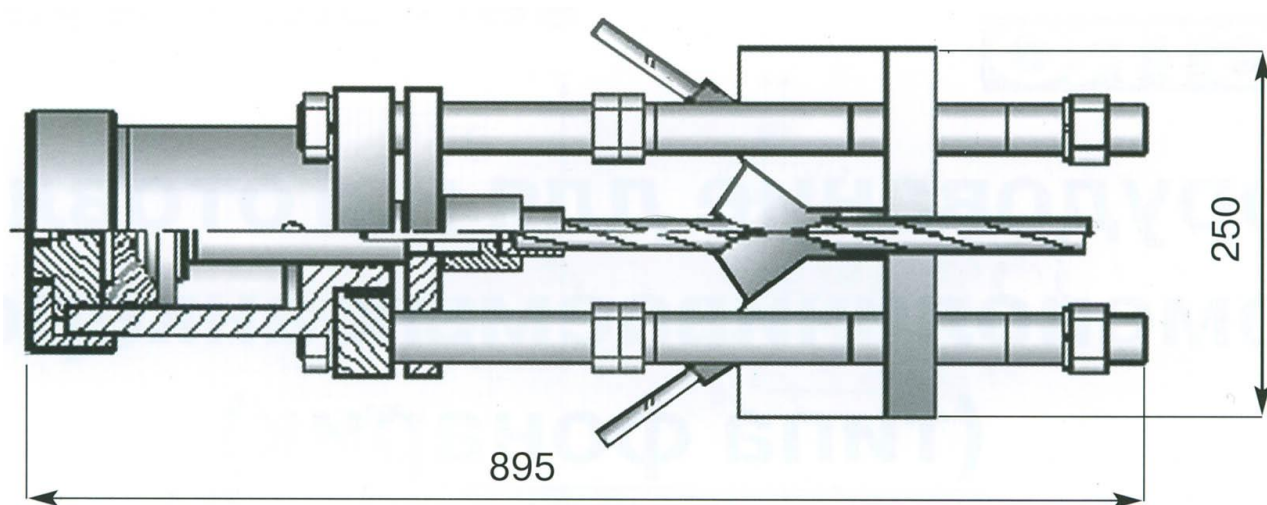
Стенд ГПФ-3 для осуществления расплетения проволок на конце каната 15К7 с формированием «фонарика», обеспечивающего самоанкеривание каната в бетоне без использования специальных анкеров.
